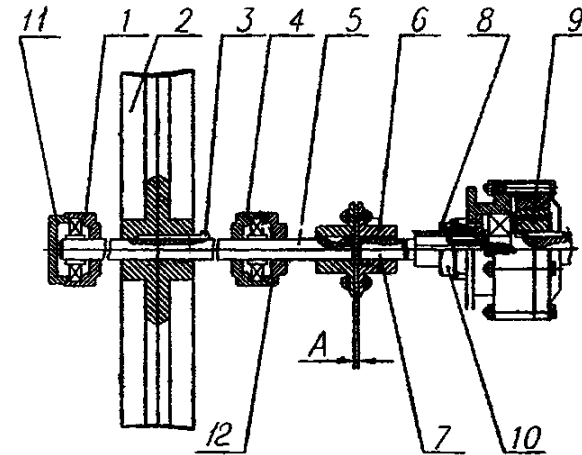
Вал привода: Кир.23.0.0000-02
